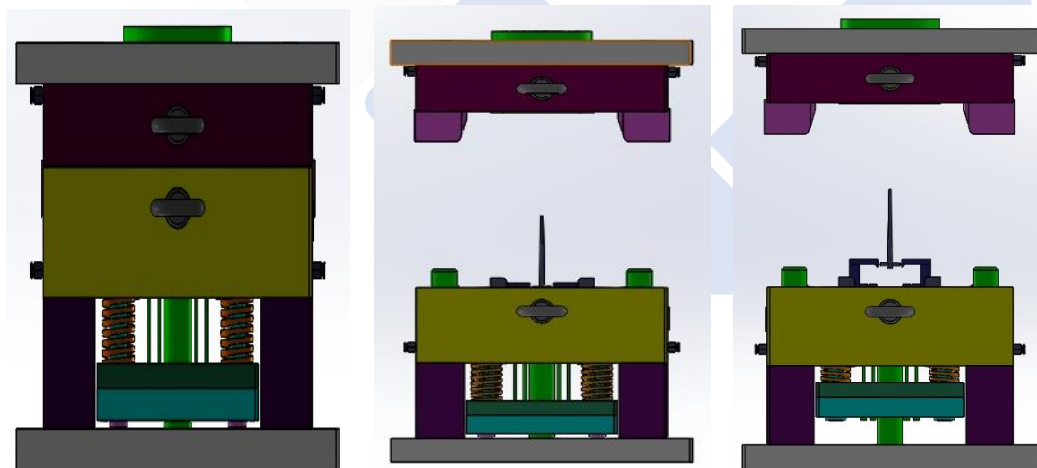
Proses Assembly Desain Cetakan Produk *Holder
